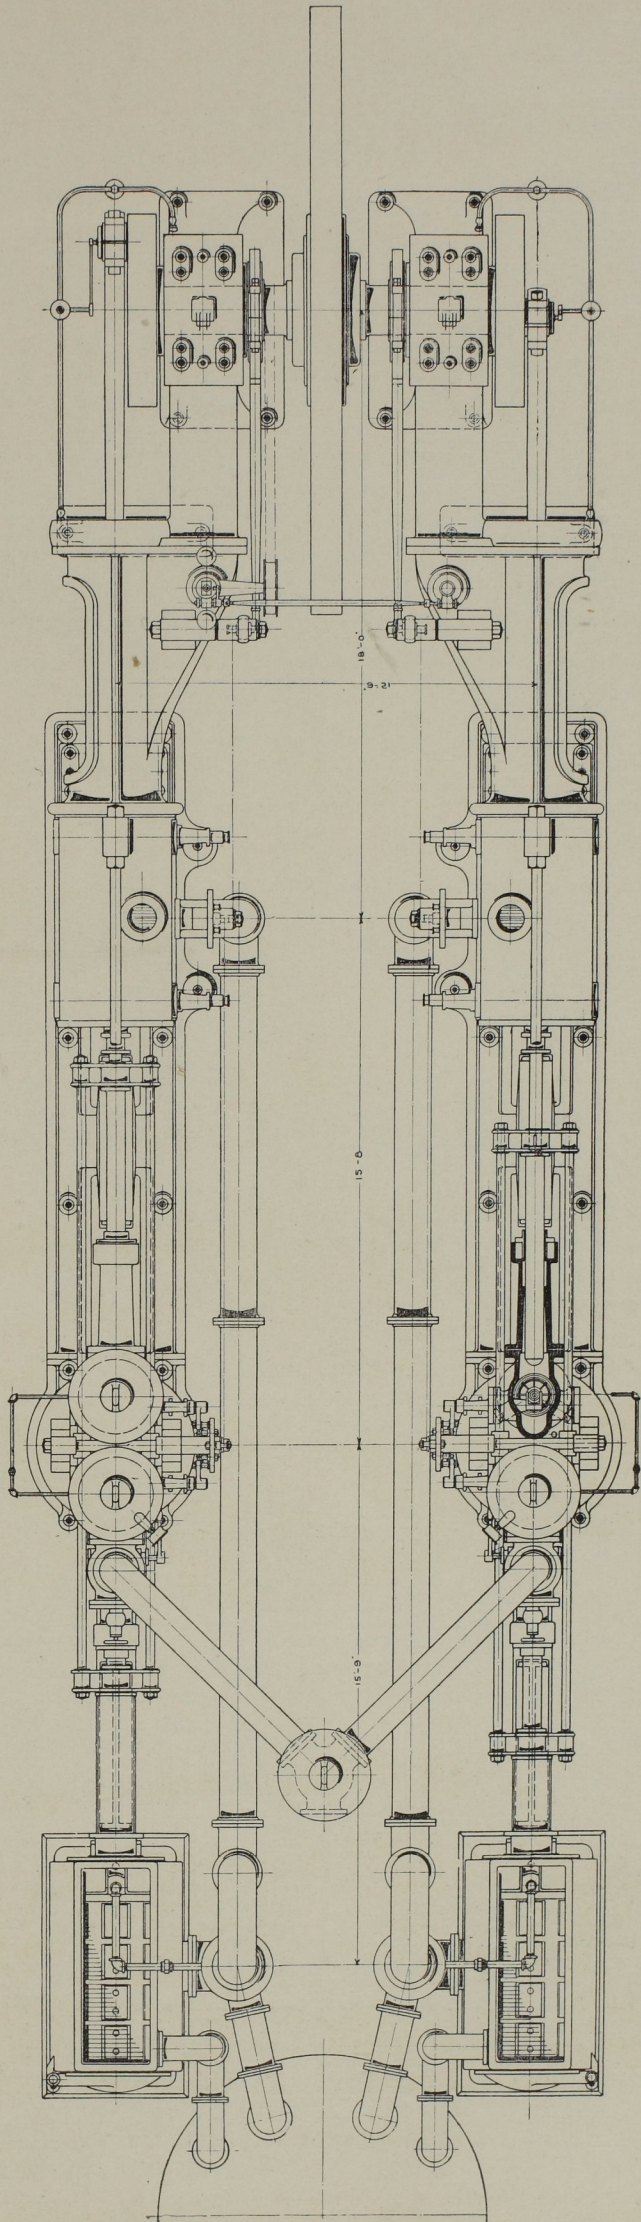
Grundriss. Massst. 1 : 64.
